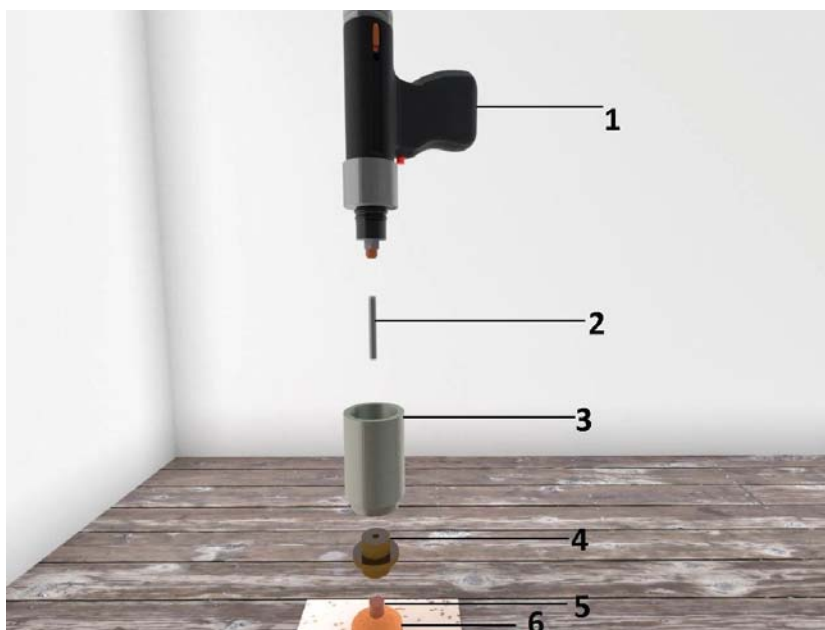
Сварочный пистолет с дополнительным прижимным устройством:
